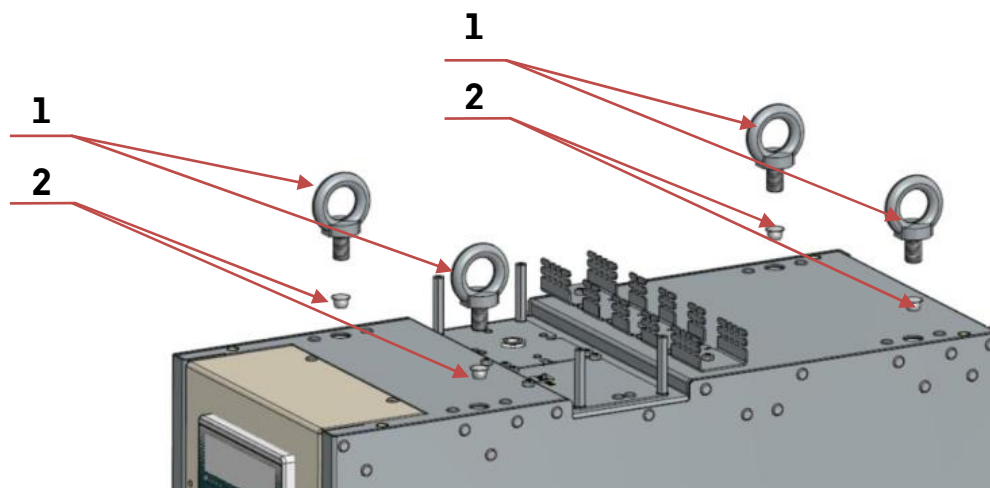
Установка резиновых заглушек вместо рым-болтов
